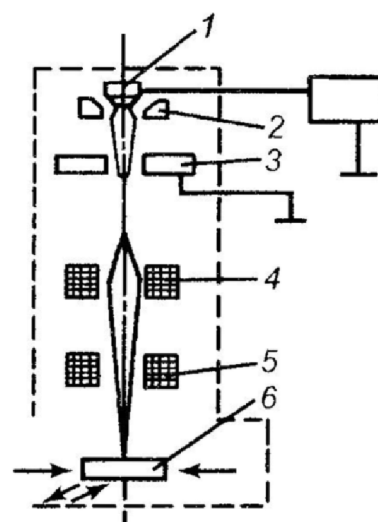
Схема установки для электронно-лучевой сварки:
